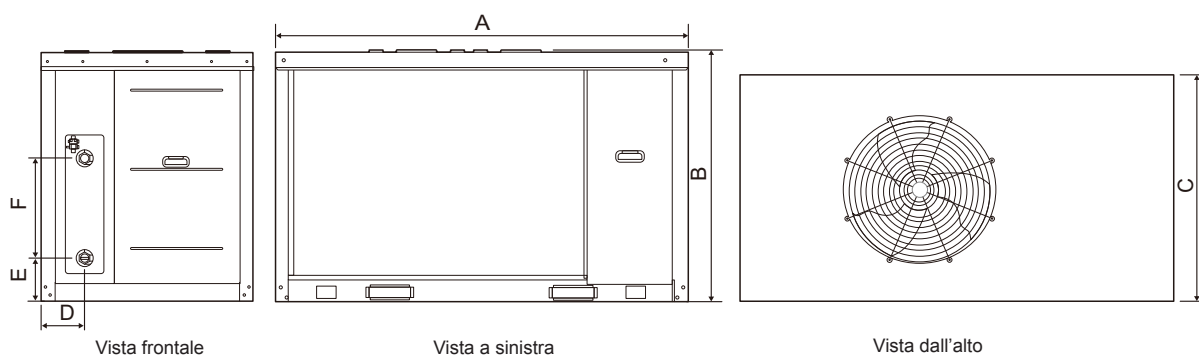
Dimensione d'insieme di KEM-30 DRS4.1
